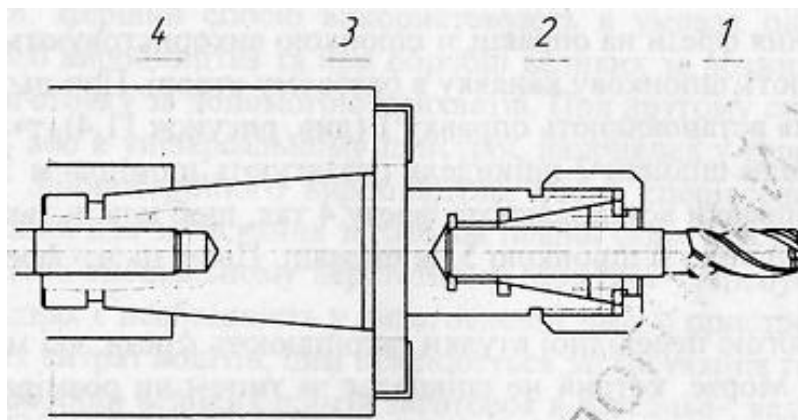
Схема закріплення фрези в цанговому патроні
